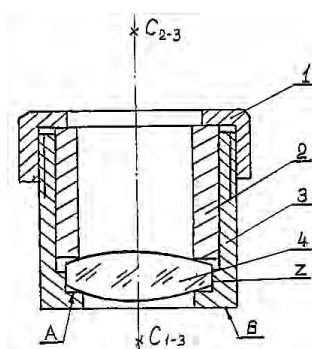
Экспериментальный корпус объектива: 1 – гайка (Д16); 2 – кольцо (ЛС-59); 3 – корпус (ЛС-59); 4 – линза №30
